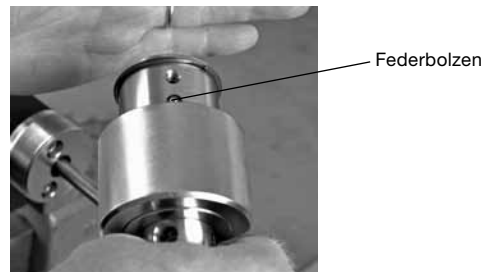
Das Ende des Anfaswerkzeug freilegen
